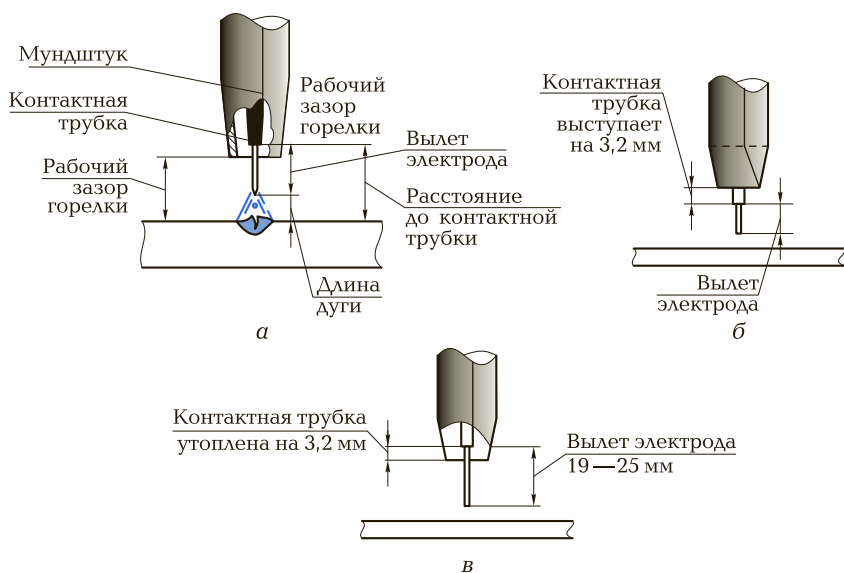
Вылет электродной проволоки из мундштука сварочной горелки (а), расположение контактной трубки в сопле горелки при циклическом режиме сварки короткой дугой (б) и струйном переносе металла (в)
